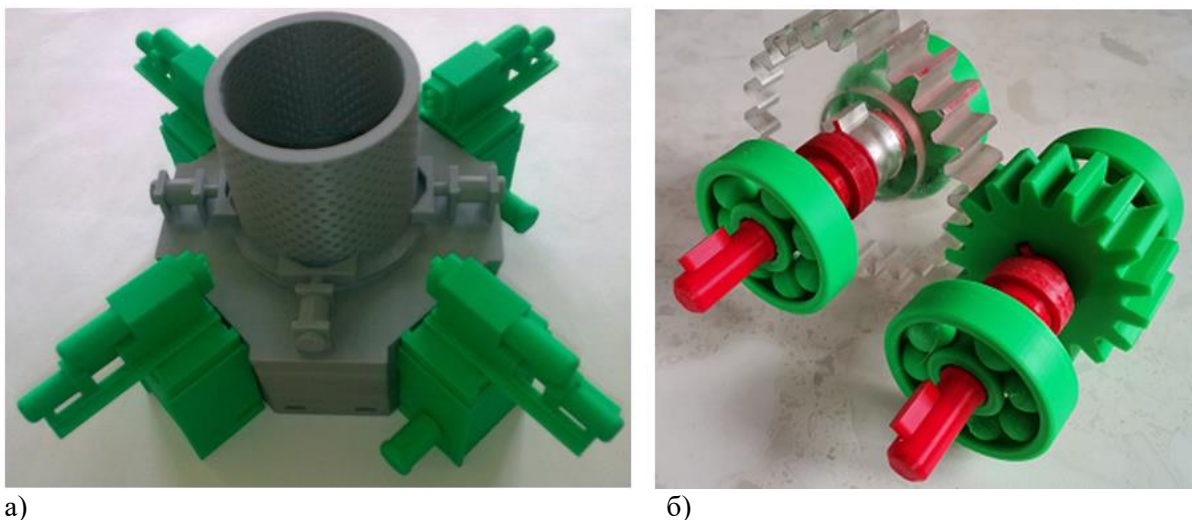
Агрегатный станок для изготовления цилиндрических матриц гранулятора (а) и зубчатая цилиндрическая передача коробки подачи токарно-винторезного станка (б), выполненные 3D-прототипированием в «Центре прототипирования КС-54»
